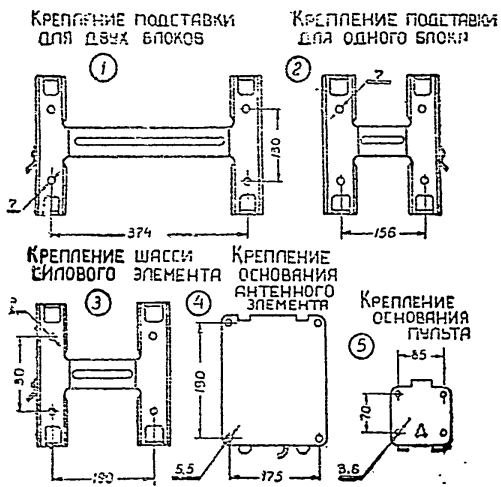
Габаритные размеры креплений элементов радиостанции.
